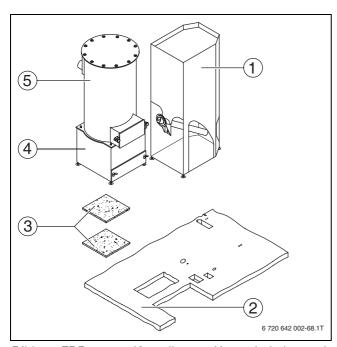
FBP 26-15: Kesselkörper, Vorratsbehälter und Kesselisolierung
